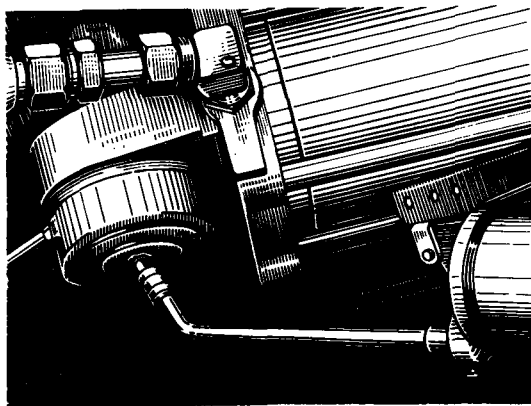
Смазка пальцев гидроцилиндров систем управления поворотом и навесного устройства
